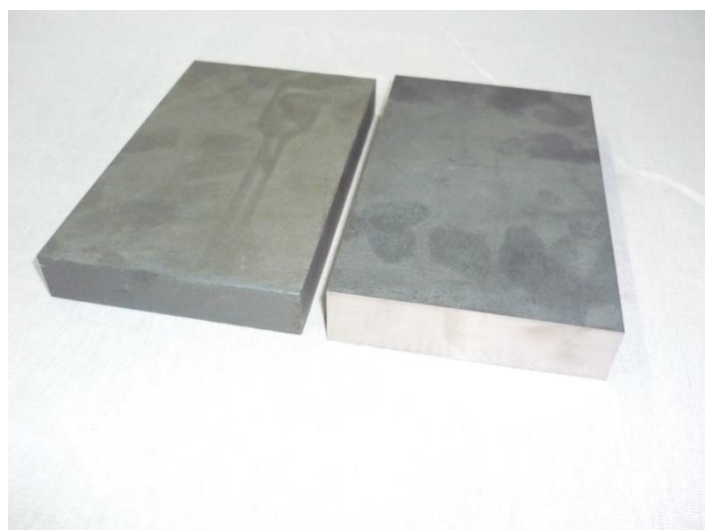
Заготовки под сварку встык из титанового сплава ВТ23
